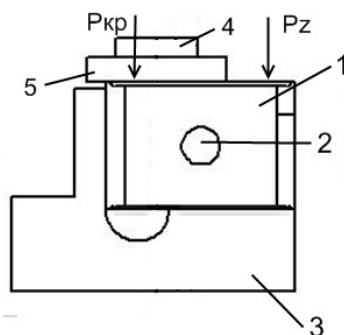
Базовая конструкция сборного реза с тангенциальным расположением пластины
